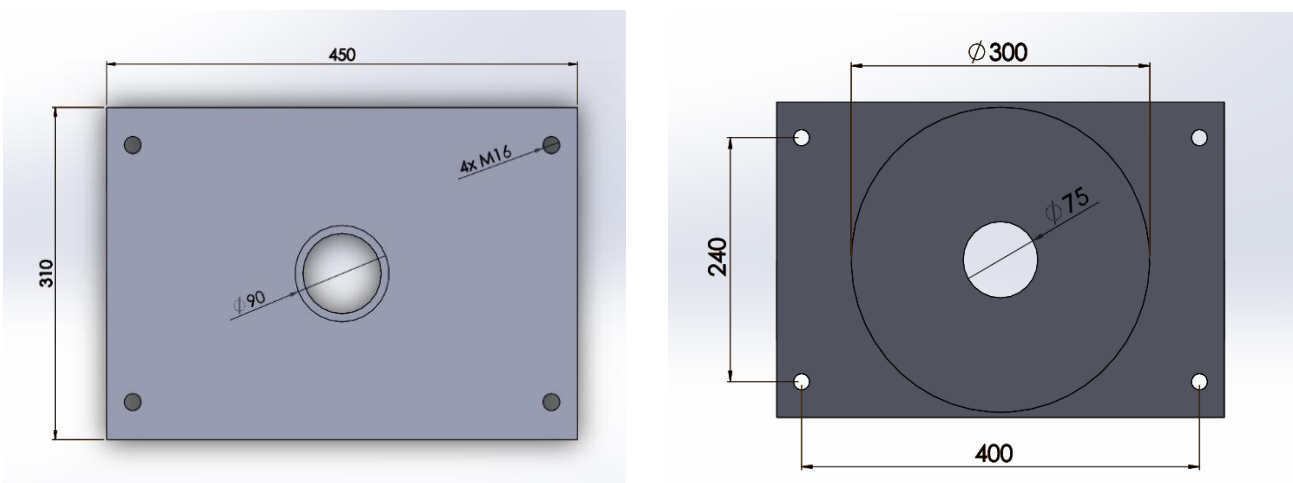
Dimensiones de la placa de apoyo del rodamiento superior.
